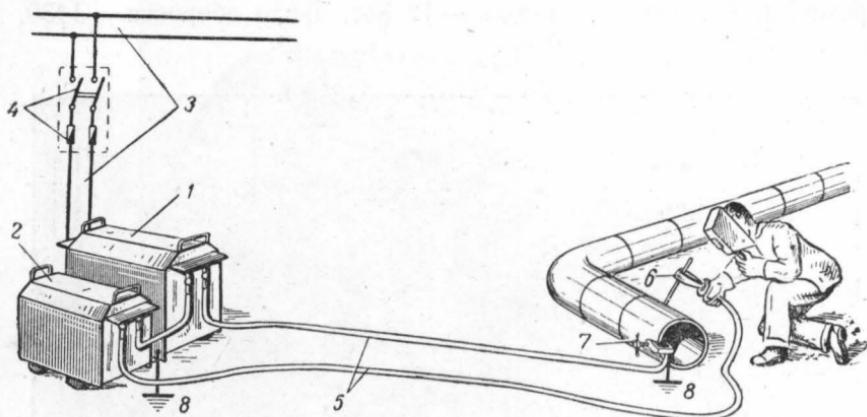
Схема установки для сварки постоянным током:
